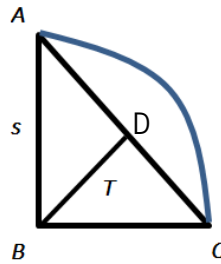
Ilustração da espessura do cordão de soldadura.
